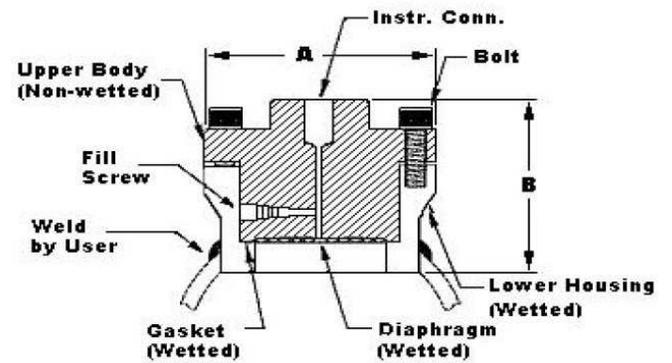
Dimensiuni Capsula Diafragma (4" Saddle Seal)
